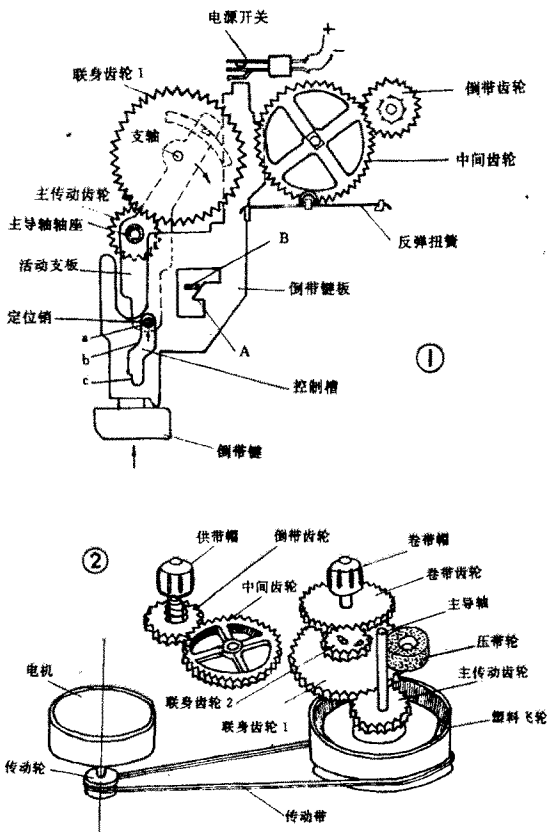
为该机心驱动机构结构原理图。电机通过一条传动带驱动飞轮、主导轴旋转。在塑料飞轮的上端面设有与其一体的主传动齿轮, 主传动齿轮与联身齿轮1啮合, 联身齿轮2和卷带齿轮构成长期啮合对。中间齿轮与倒带齿轮为长期啮合对。从图1中不难看出, 该机心录放音和快进状态的传动路线完全一致。当按下放音键后, 磁头滑板前进, 接通电机电源, 同时带动压带轮与主导轴压贴。固定在电机轴头上的传动轮驱动传动带, 带动飞轮旋转, 由主传动齿轮带动联身齿轮1转动,
